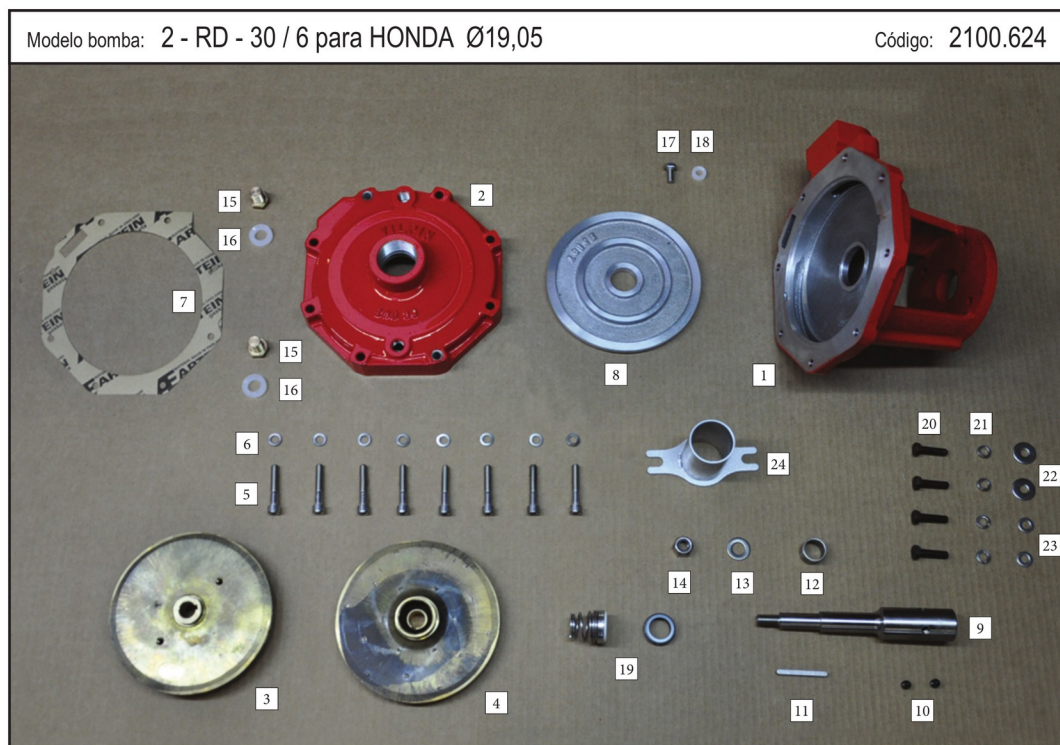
Vista explodida da bomba 2-RD-30/6 (AY-H 130 AP · AY-KT 130 AP)
